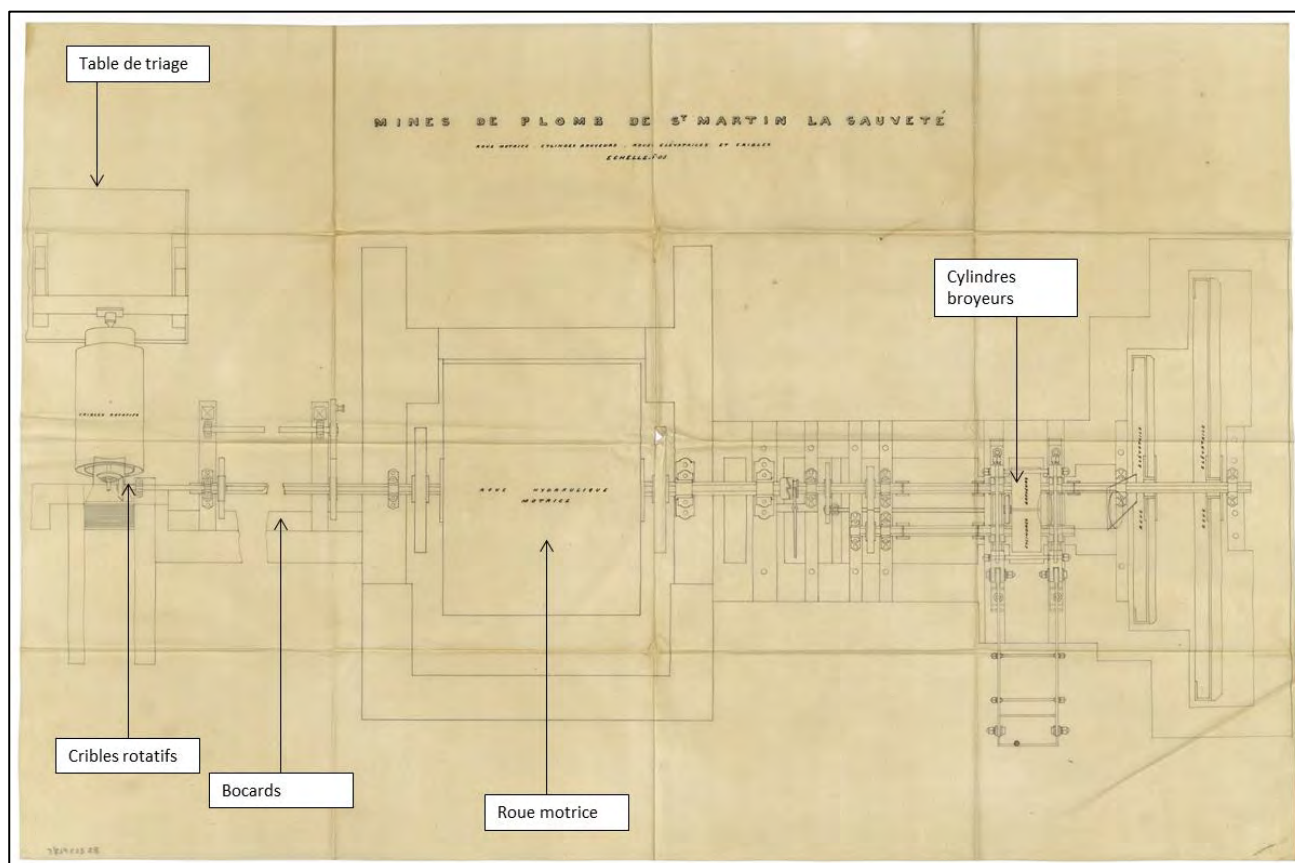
Site de Grézolles - Plan de détail des installations de broyage
